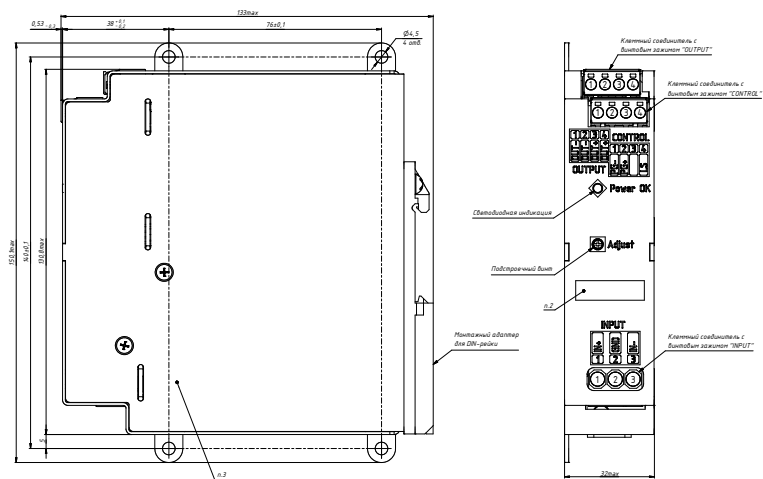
Габаритный чертеж для исполнения VDD75TNF.
